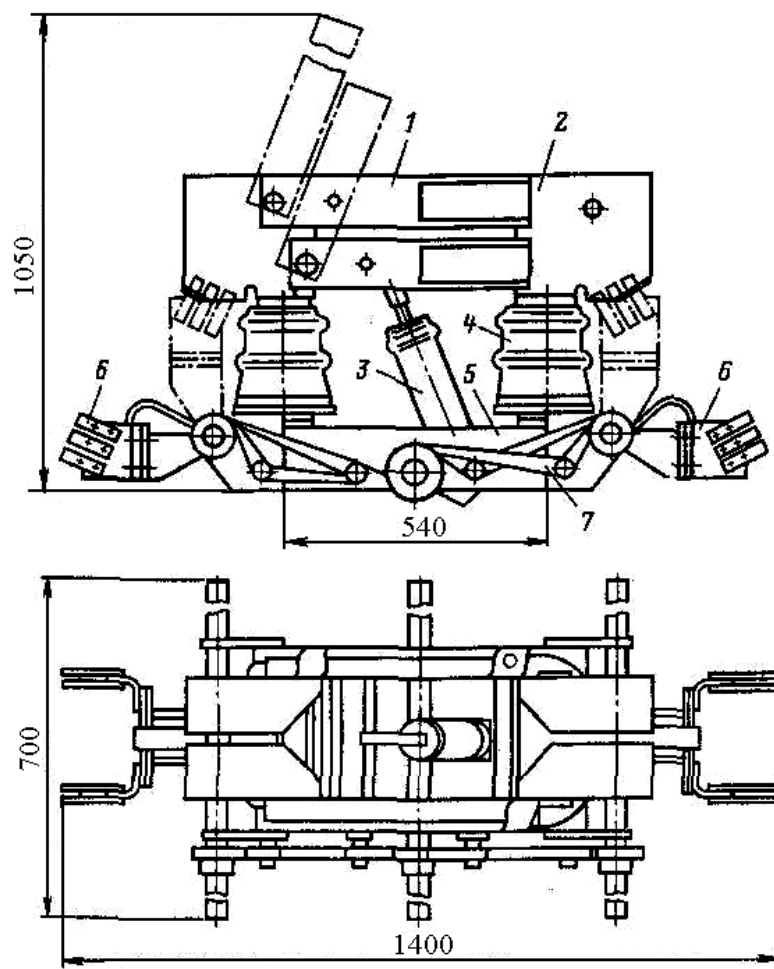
Роз'єднувач рубаючого типу для внутрішньої установки з двома заземлюючими ножами РВЗ-2-20/8000:
